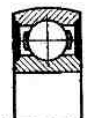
Шарикоподшипник со сферической поверхностью наружного кольца
